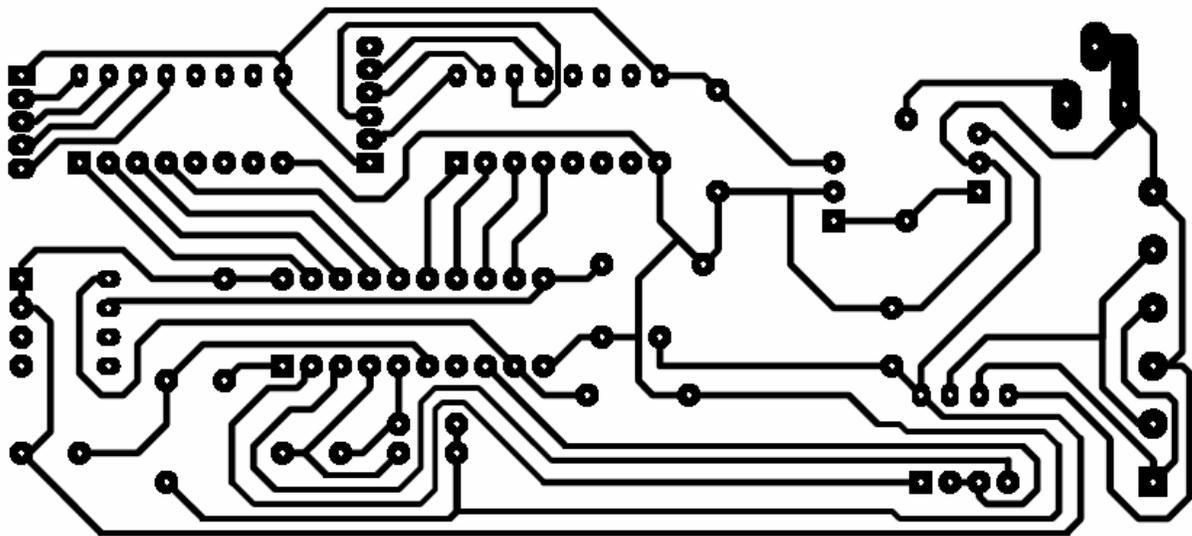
Circuito impreso de la unidad de Pan/Tilt (lado de la soldadura).
